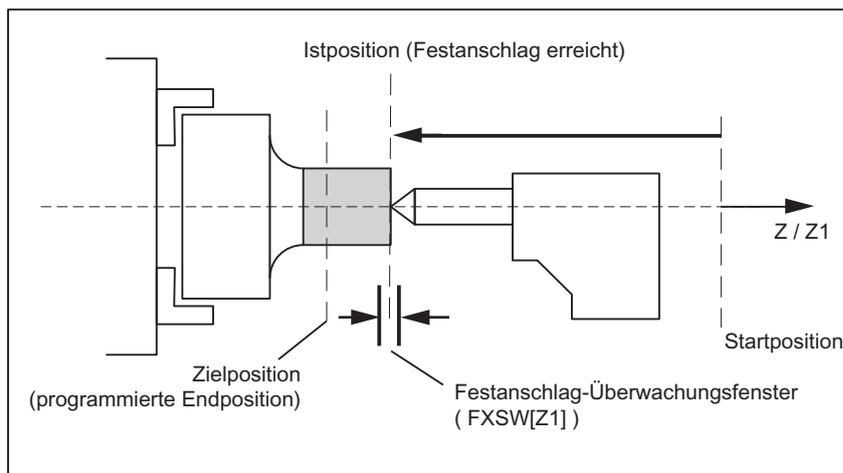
Beispiel für Fahren auf Festanschlag, Pinole wird auf das Werkstück gedrückt
